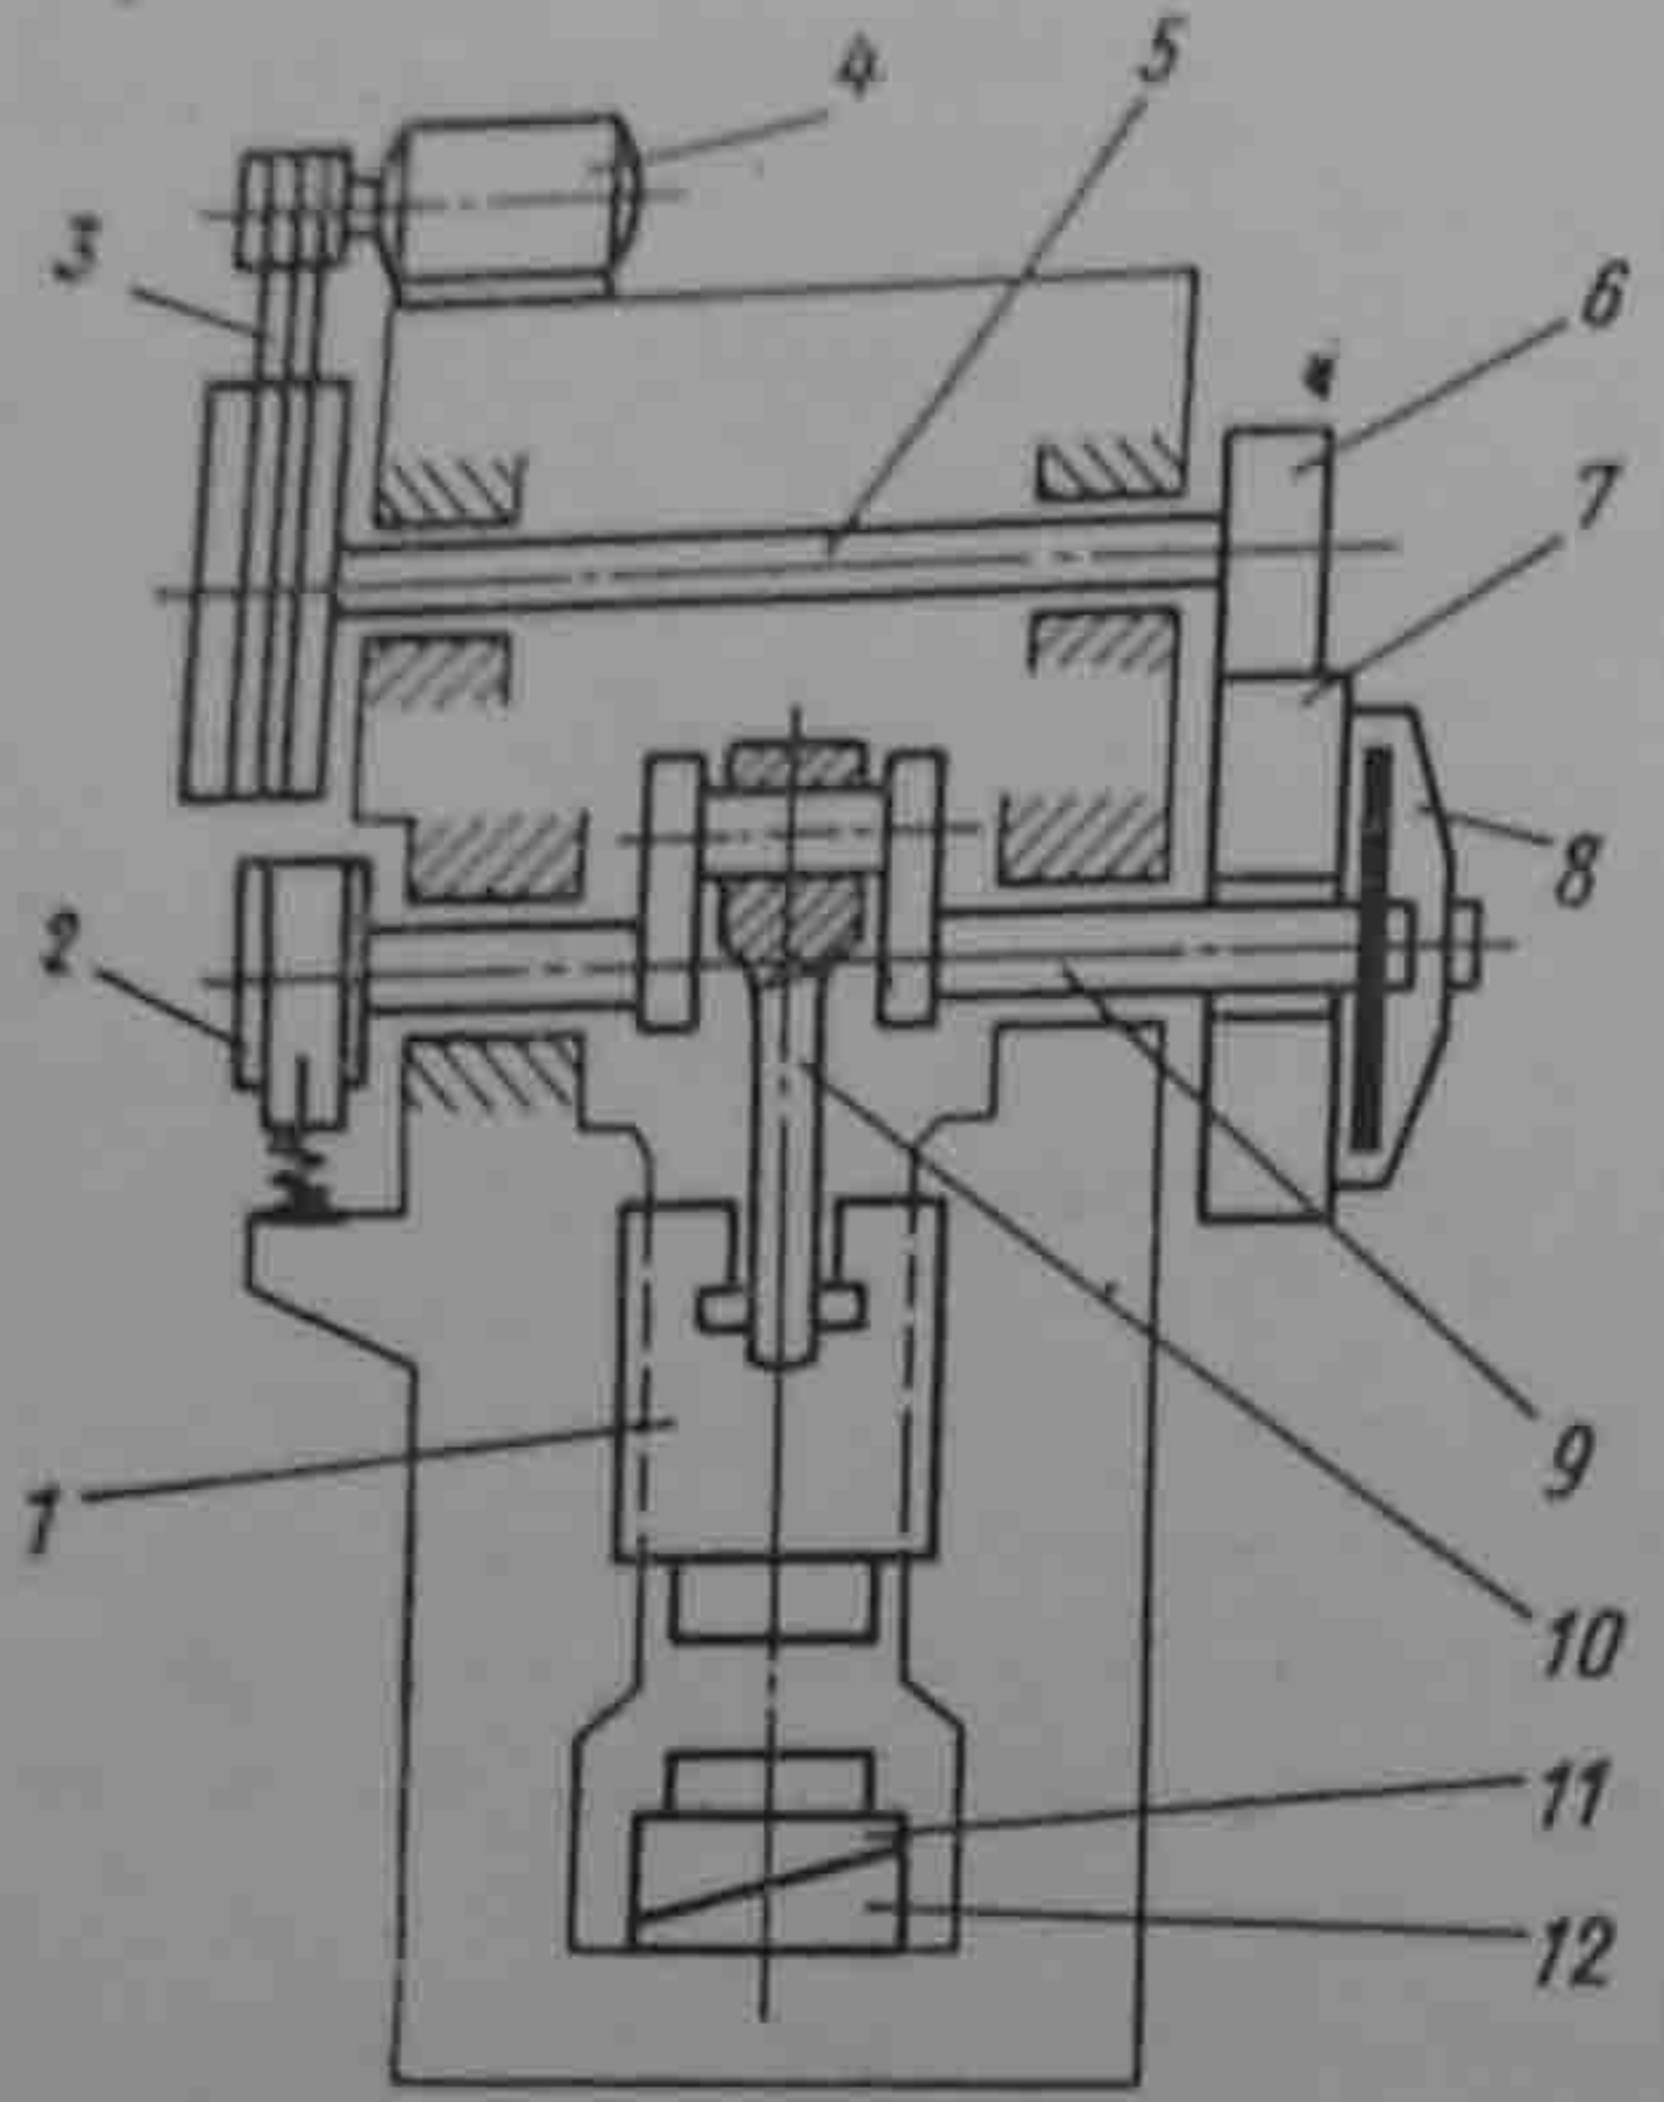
Кинематическая схема кривошипного горячештамповочного прессы
